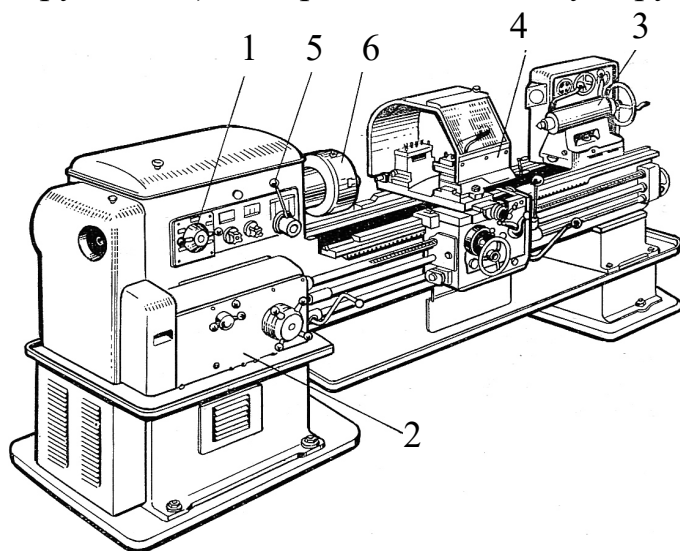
Токарно-гвинторізний верстат: 1 – коробка швидкостей; 2 – коробка подач; 3 – задня бабка; 4 – супорт; 5 – рукоятка керування; 6 – пристосування для закріплення заготовки (патрон)
